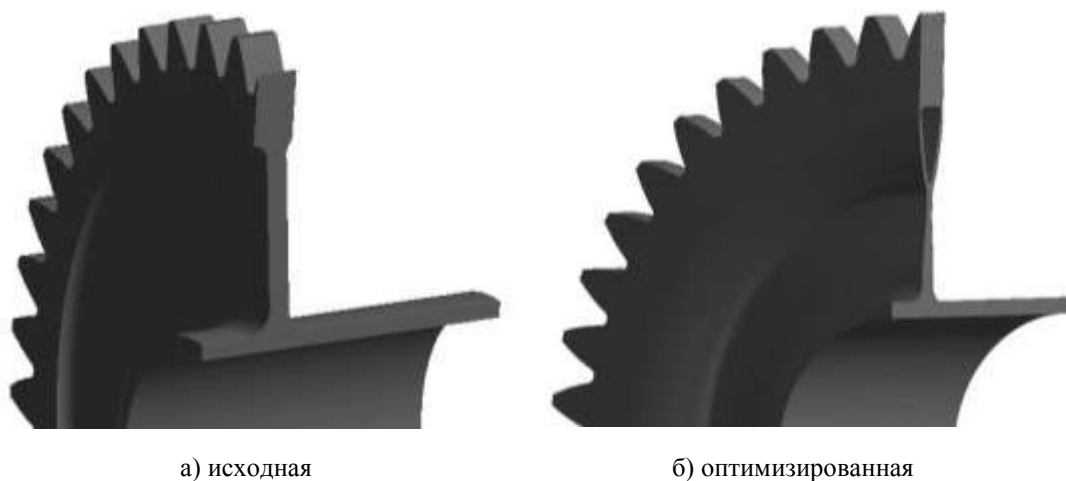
Модели конструкции прямозубой шестерни привода вентилятора
